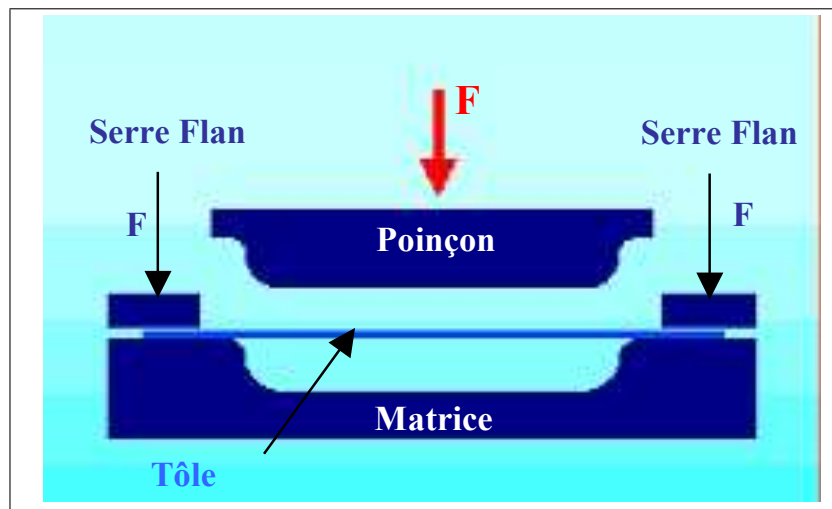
Procédé d'emboutissage : Photo [Emb02]
